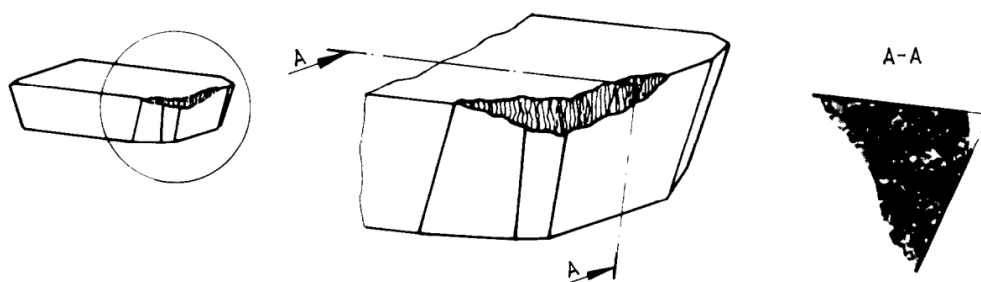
Desgaste de flanco uniforme (VB 1) [34].
